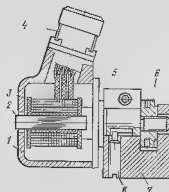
Датчик измерителя эксцентриситета ротора. 1 — крышка; 2 — сердечник; 3 — катушка; 4 — индуктивный датчик; 5 — катушка; 6 — гайка; 7 — винт; 8 — фиксатор.
